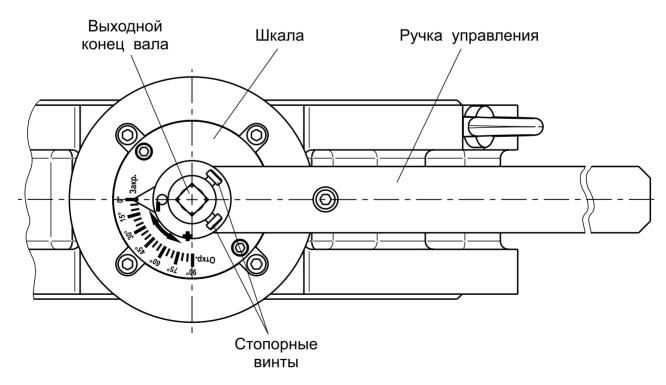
Заслонка регулирующая с ручным управлением (вид сверху)
